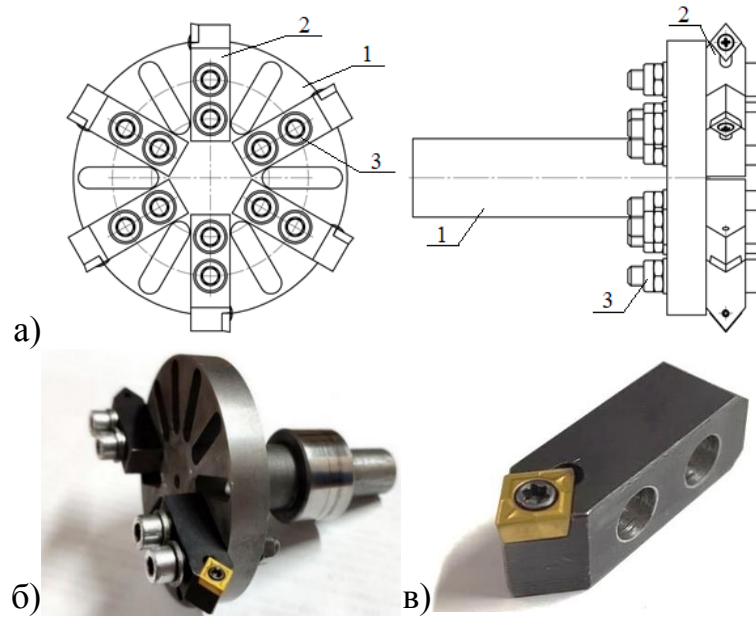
Конструкция резового блока: а) сборный чертеж: 1 – корпус резового блока; 2 – сборный резец; 3 – крепежные элементы; б) резовый блок; в) сборный резец
